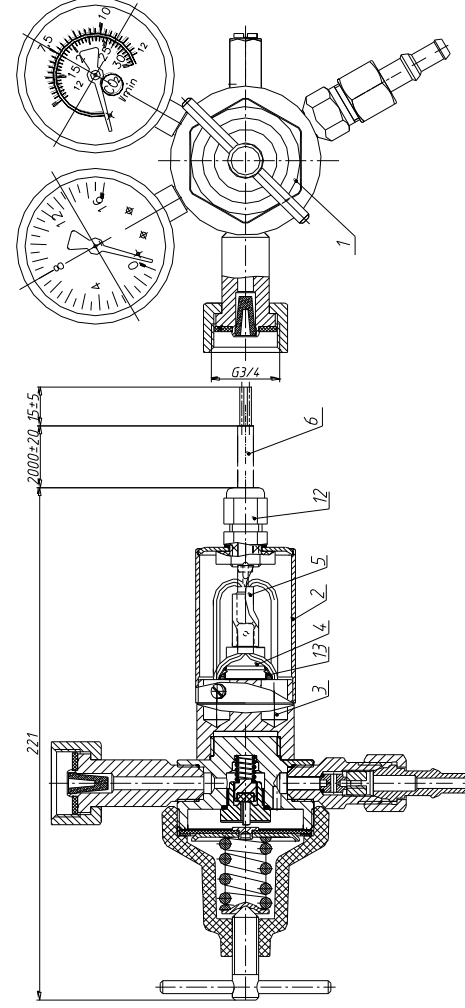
Регулятор расхода газа баллонный одноступенчатый крупногабаритный с подогревателем У-30-КР2П:
